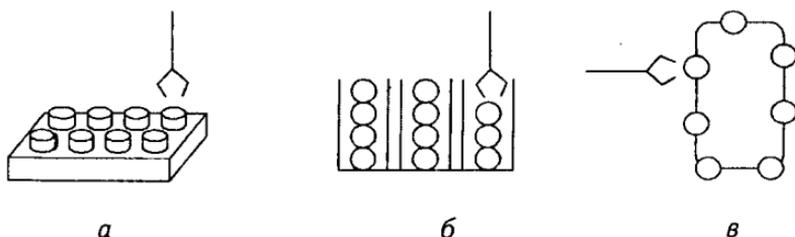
Схемы накопителей: *а* — кассета; *б* — многорядный магазин; *в* — цепной накопитель
